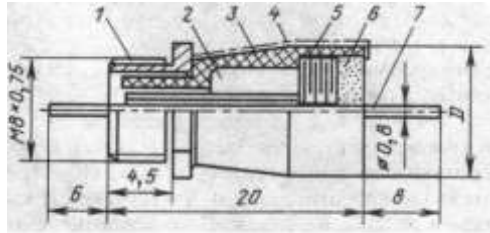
Конструкция проходного керамического фильтра: 1 — втулка; 2 — феррит; 3 — корпус; 4 — металлизированный вывод
